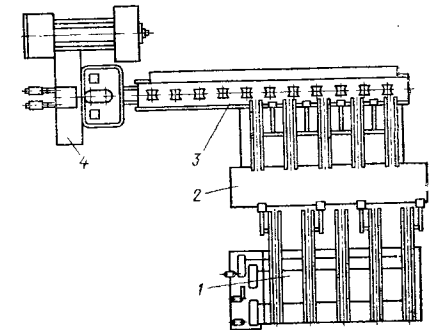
Автоматизированный комплекс для резки проката на базе сортовых ножниц усилием 10 000 кН
